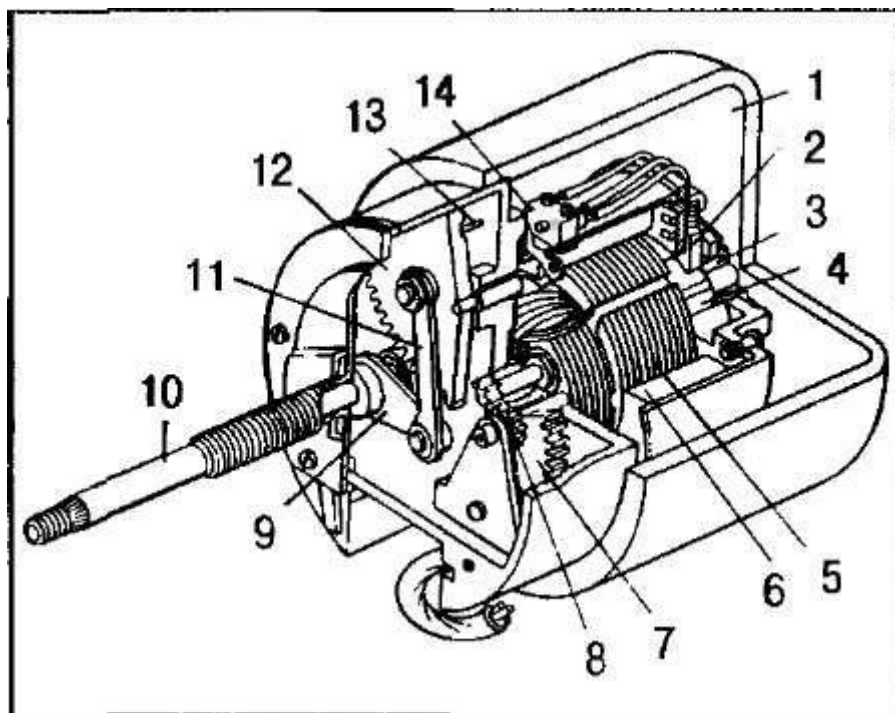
Моторредуктор очищувача фар. (1 - корпус; 2 - щітки; 3 - підшипник; 4 - колектор; 5 - ярі; 6 - постійний магніт; 7 - ведена шестерня першого ступеня редуктора; 8 - провідна шестерня другого ступеня редуктора; 9 - поводок; 10 - вихідний вал; 11 - шатун; 12 - ведена шестерня другого ступеня редуктора; 13 - шток; 14 – вимикач)
